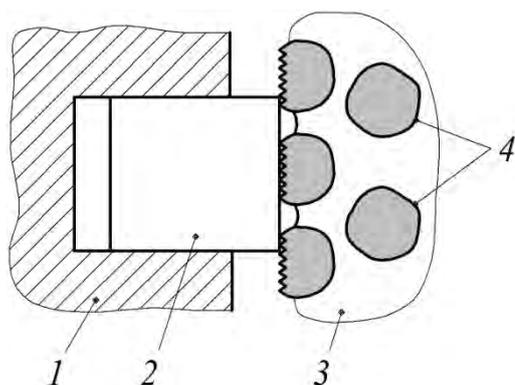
Схема взаимодействия поршневого кольца с рабочей поверхностью цилиндра: 1-поршень; 2-поршневое кольцо; 3-цилиндр блока из алюминиевого сплава; 4-кристаллы кремния
